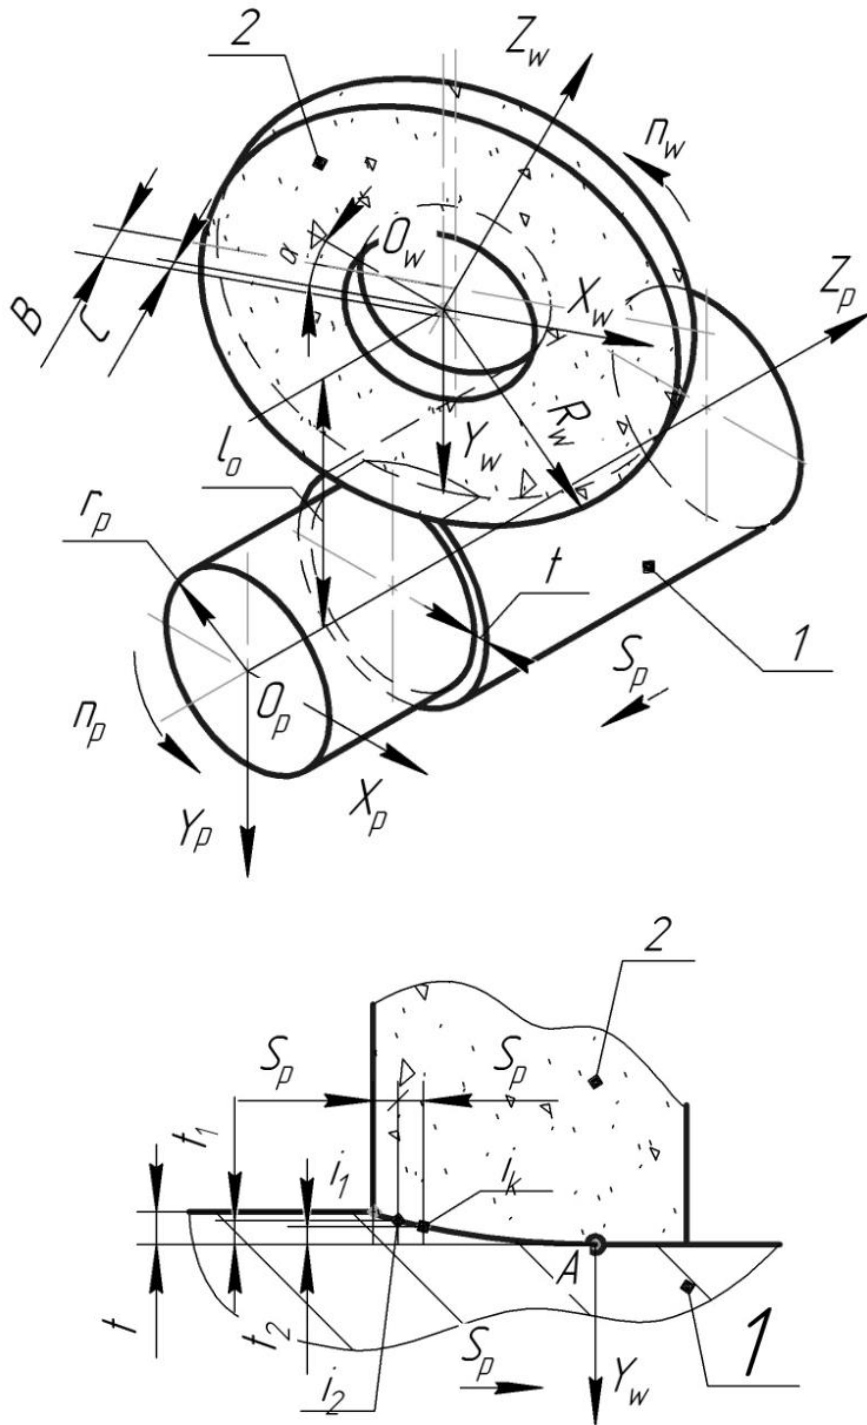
Шліфування циліндричного вала периферією орієнтованого інструмента
